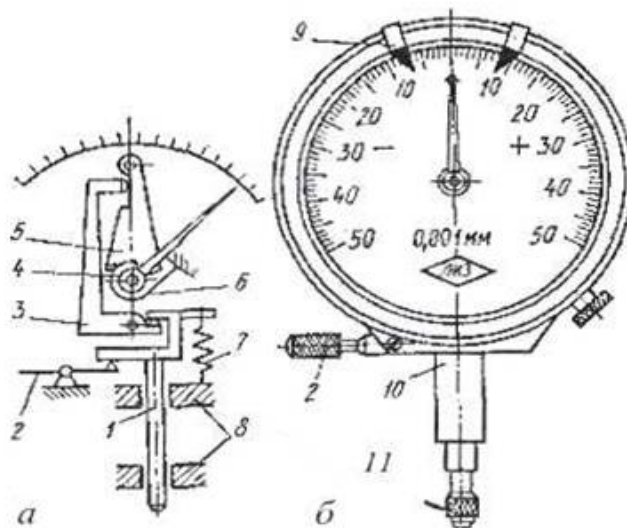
Важільно-зубчаста вимірювальна головка ІІГ (мікромір): а - схема; б - загальний вигляд: 1 - вимірювальний стержень; 2 - відвідний важіль; 3 - двоплечий важіль; 4 - зубчасте колесо; 5 - важіль з зубчастим сектором; 6 - спіральна пружина; 7 - пружина; 8 - напрямні втулки; 9 - переставні показчики поля допуску; 10 - напрямна втулка (гільза); 11 - вимірювальний наконечник
